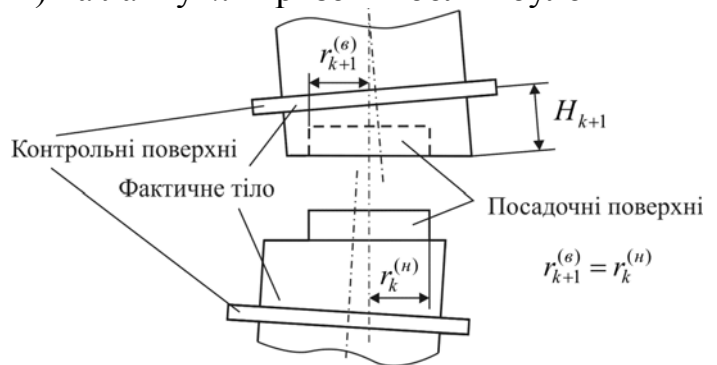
З'єднання ланок ротора за посадочними поверхнями, що неточно виготовлені
